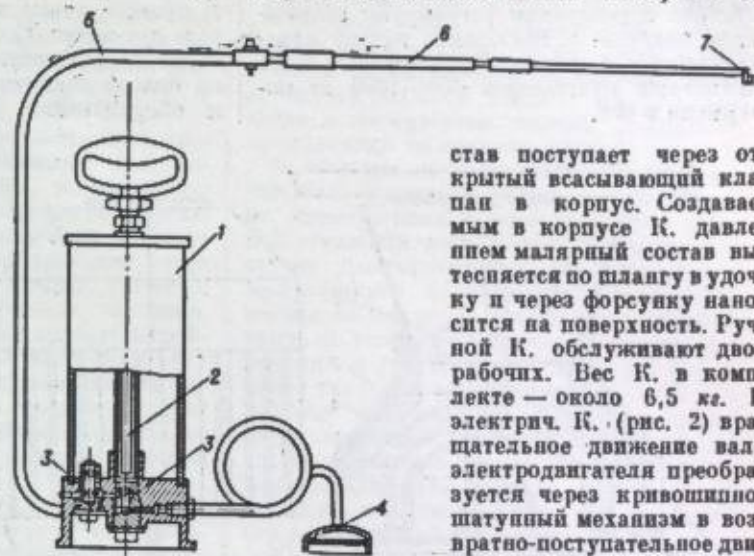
Ручной краскопульт: 1 — корпус; 2 — насос; 3 — основание с шариковыми клапанами; 4 — всасывающий фильтр со шлангом; 5 — магнетальный шланг; 6 — удочка; 7 — форсунка.
